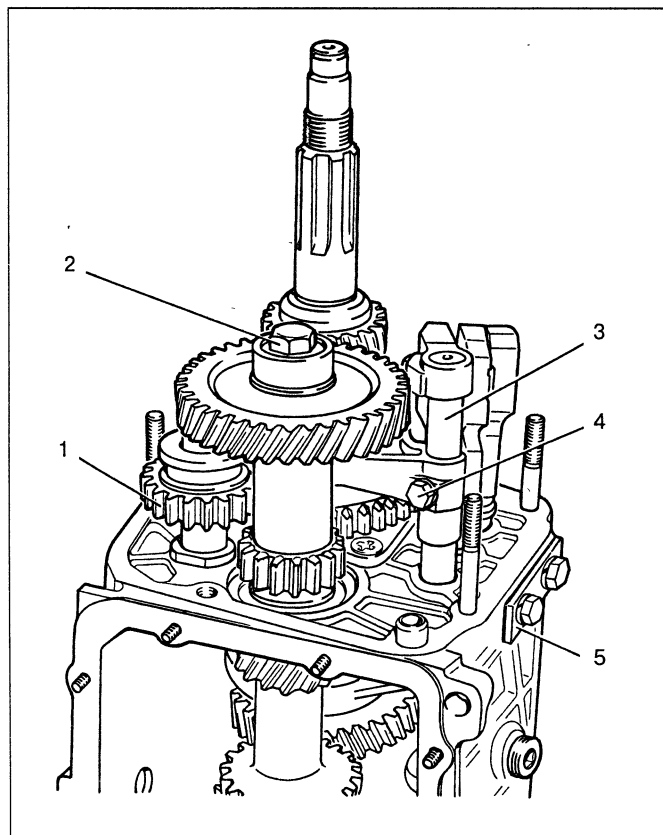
Отвертывание болтов крепления блока шестерен и вилки включения V передачи и заднего хода: 1 – промежуточная шестерня заднего хода; 2 – болт крепления блока шестерен; 3 – шток вилки; 4 – болт крепления вилки; 5 – крышка фиксаторов
